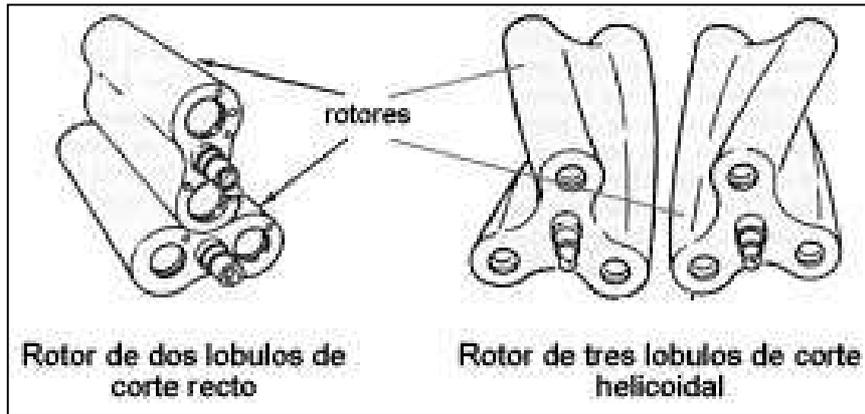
Tipos de Rotor de Compresor Roots
